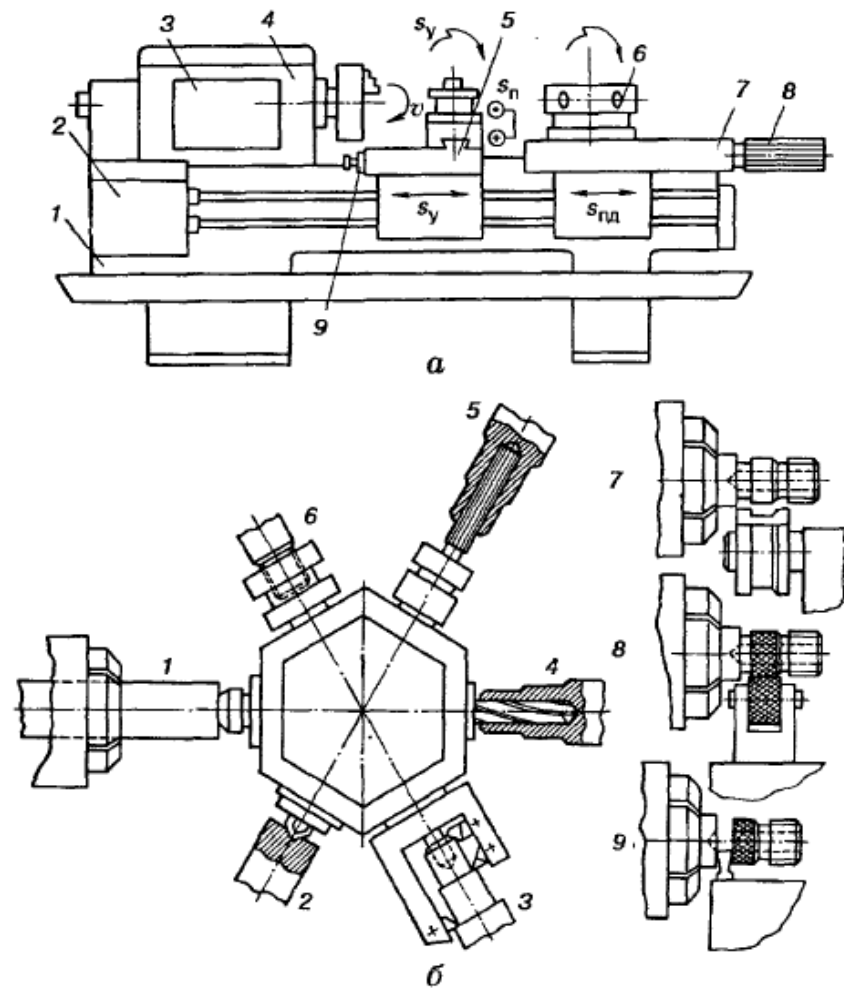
Токарно-револьверний верстат з вертикальною віссю револьверної головки
